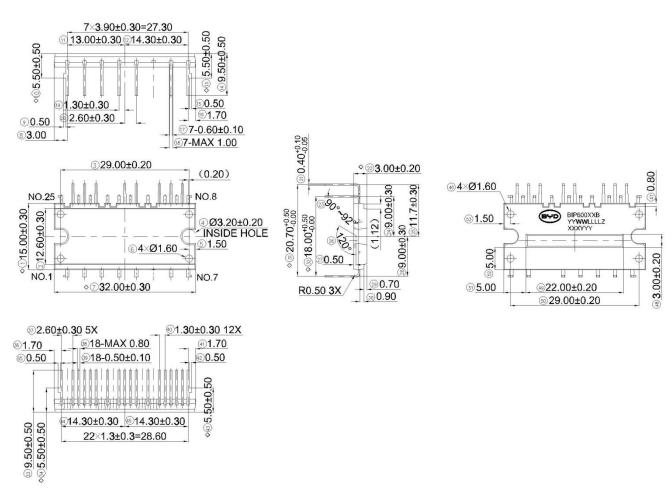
封装轮廓详图 Fig 11.Detailed Package Outline Drawings
